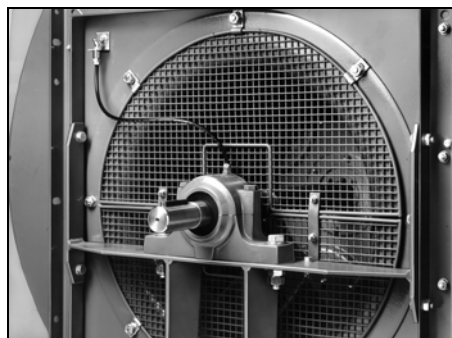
Steh-Gussgehäuse mit Pendelkugellager
